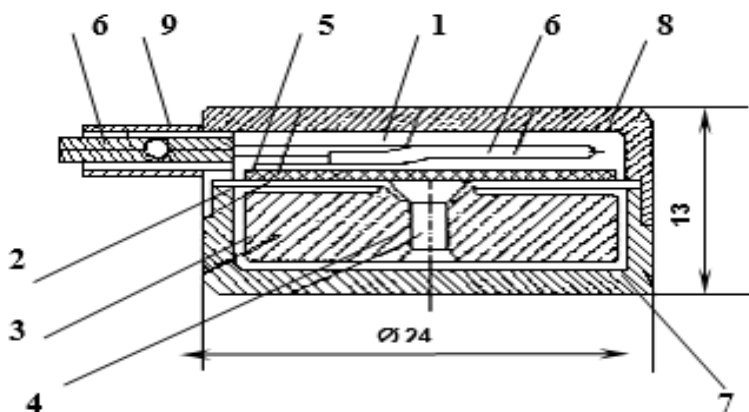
Конструкция акселерометра ПАМТ-1: 1 – пьезопластина (ЦТС-19); 2 – металлическая подложка; 3 – груз; 4 – заклепка; 5 – контактная пластина; 6 – антивибрационный кабель; 7 – корпус; 8 – крышка; 9 – втулка
